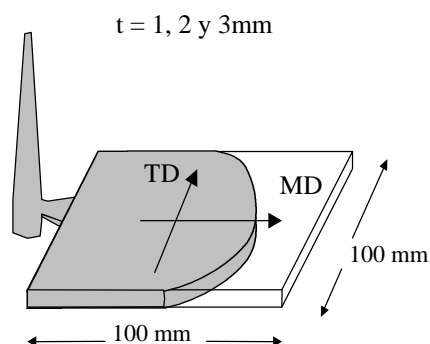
Esquema del llenado del molde de las placas indicando las dimensiones y orientaciones principales.
